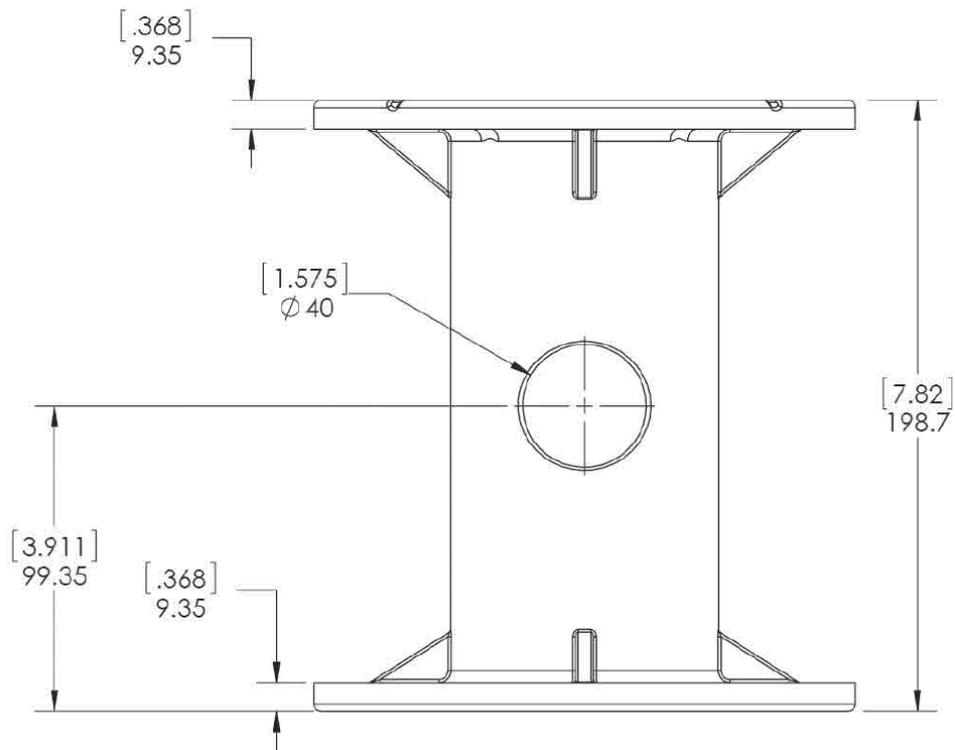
Надпалубное оборудование (ADE) - Вид снизу
